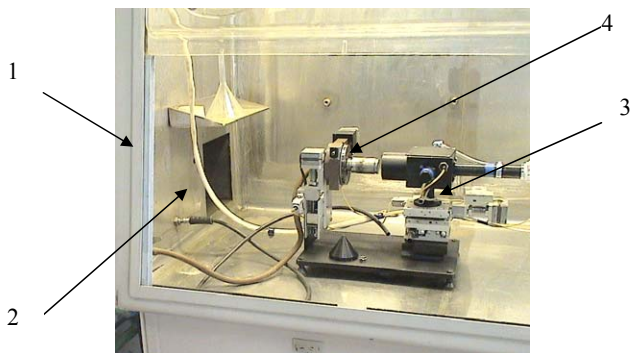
Общий вид установки лазерной сварки, размещенной в боксе:
